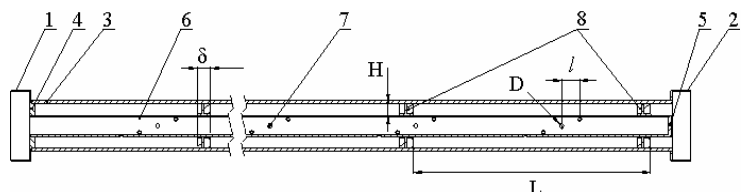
Струминно-вихровий рекуператор: 1 — вхідний повітряний короб; 2 — вихідний повітряний короб; 3 — нагрівна труба; 4 — вхідна перфорована кришка; 5 — заглушка; 6 — внутрішня повітряна труба; 7 — отвори-сопла; 8 — лопаті у формі гвинтової крильчатки.
